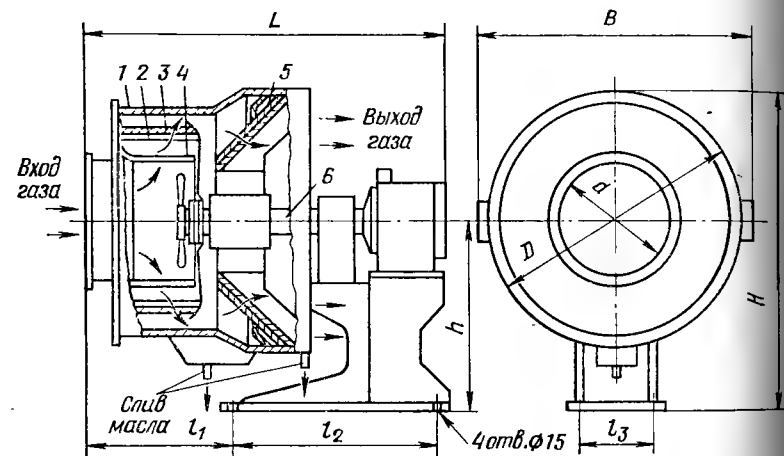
Ротационный фильтр типа ФРМ для улавливания масляного тумана: 1 — корпус; 2 — фильтрующий материал; 3 — перфорированный барабан; 4 — вентиляторное колесо; 5 — брызгоуловитель; 6 — вал
